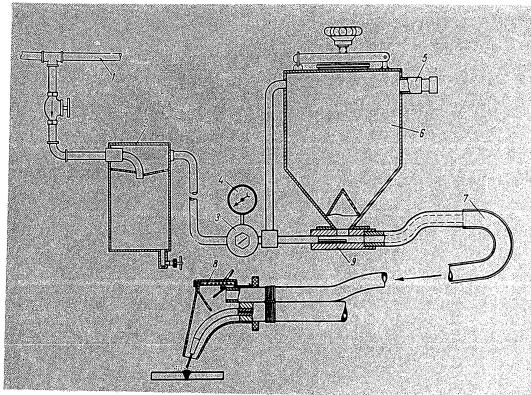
Схема пневматического устройства полуавтомата ПДЦ-500
